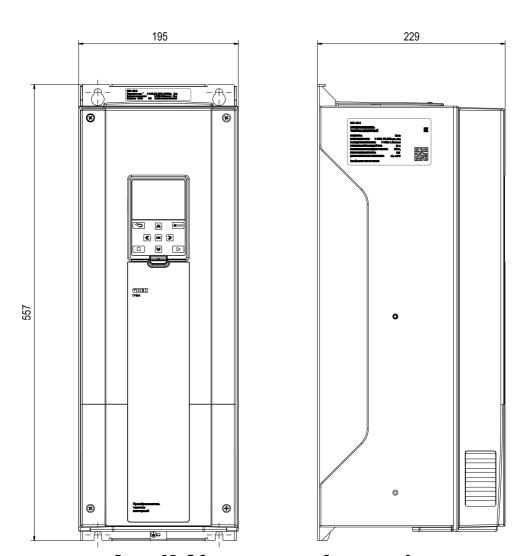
Габаритные размеры прибора в корпусе 3
